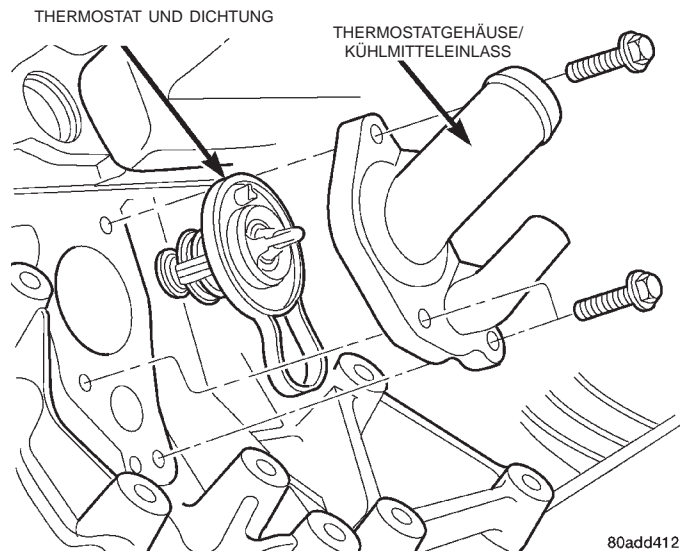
Thermostat und Thermostatgehäuse—2.7L-Motor
